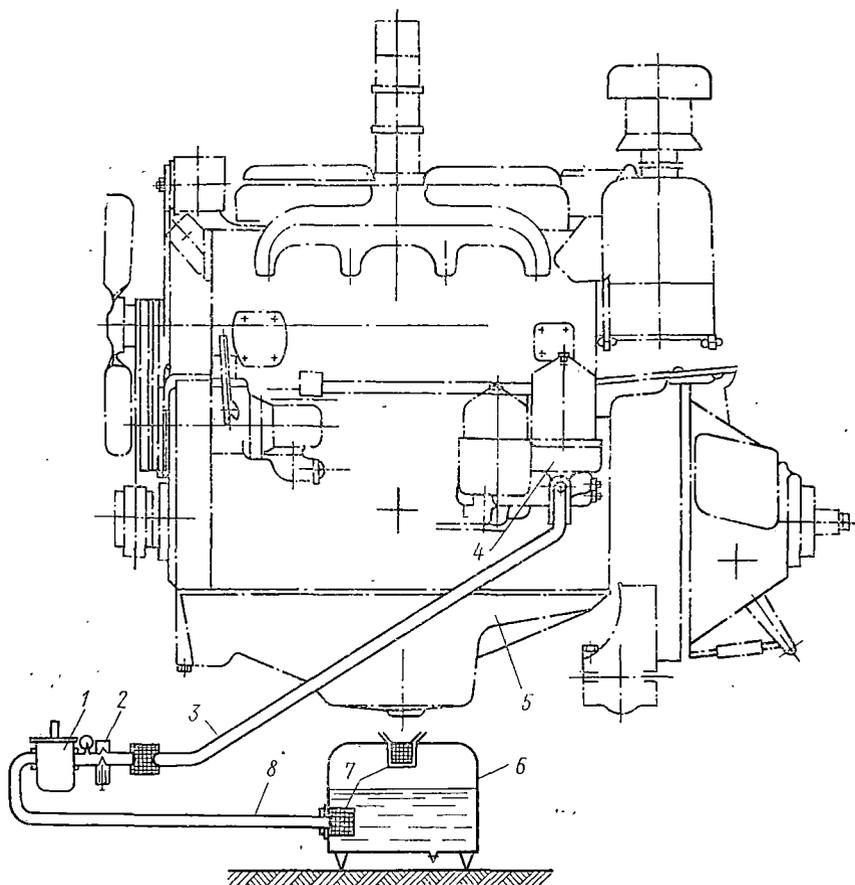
Схема приспособления для промывки системы смазки двигателя прокачкой жидкости:
